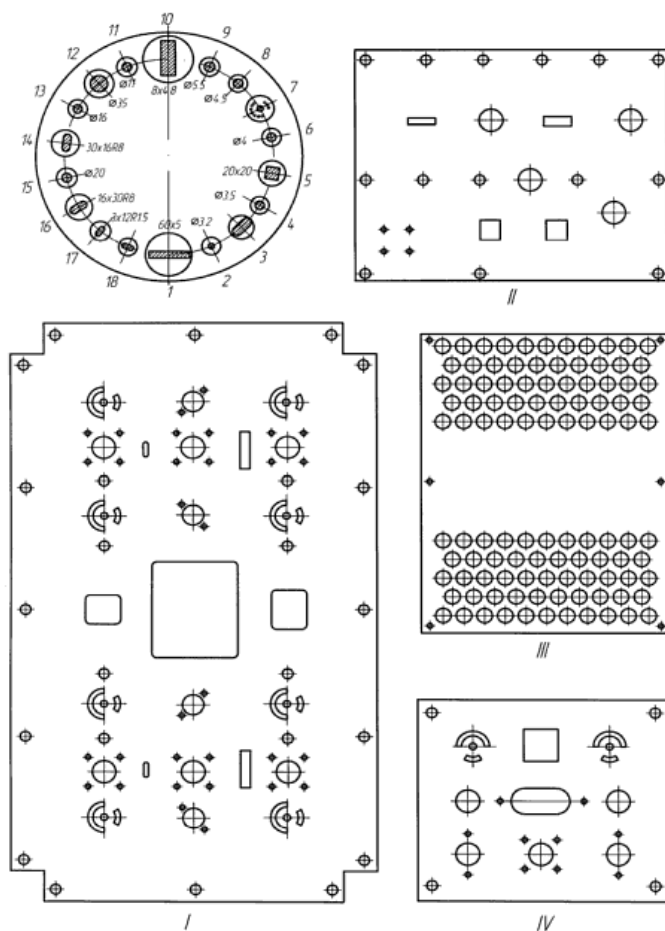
Схема револьверної головки та деталі: I, II, III, IV, які виготовлена за її допомогою
